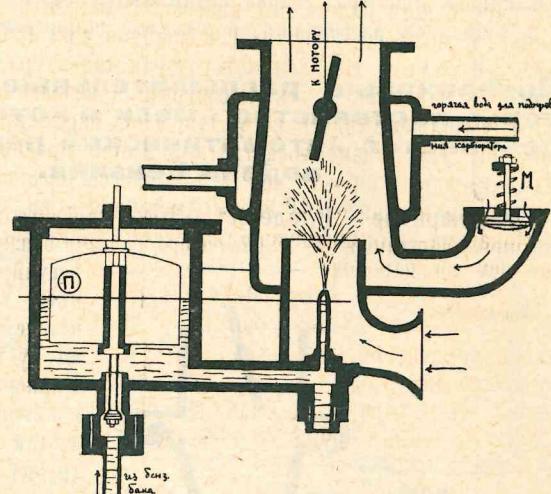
Схема устройства и действия карбюратора с автоматическим впуском воздуха. Как видно из рис., поплавковая камера здесь несколько другого устройства.
